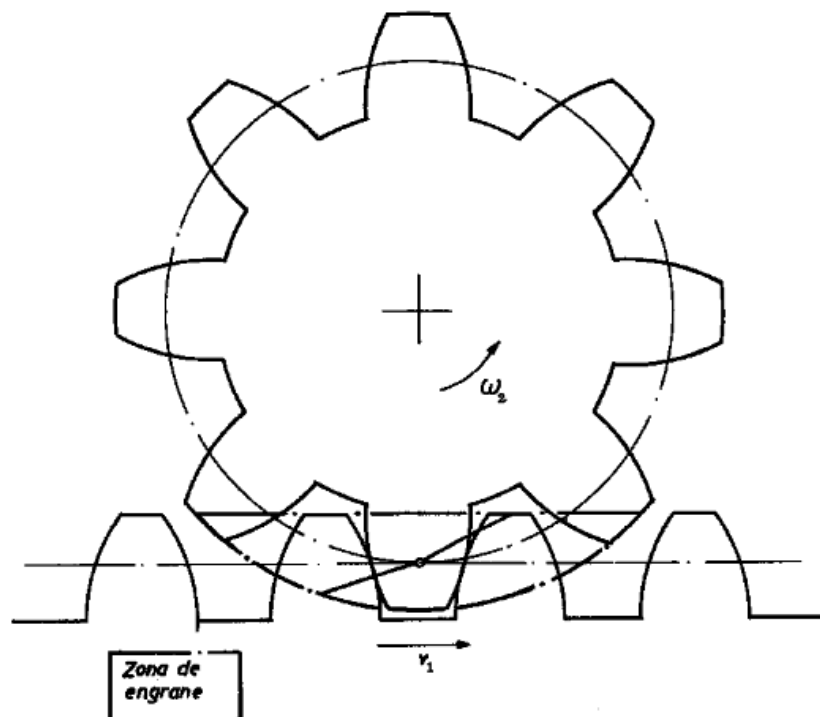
Zona de engrane entre rueda dentada y cremallera
